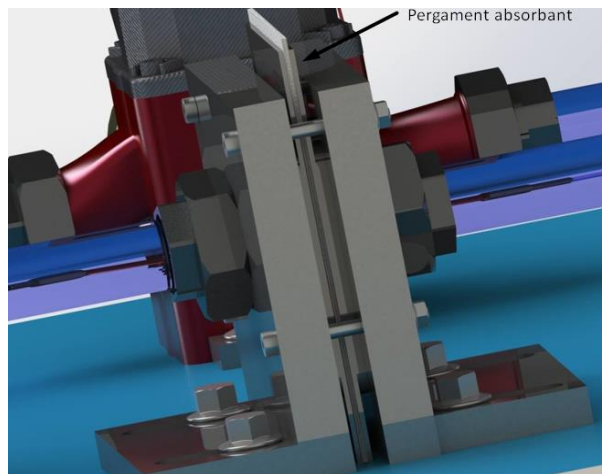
Detaliu zonă fixare pergament absorbant
